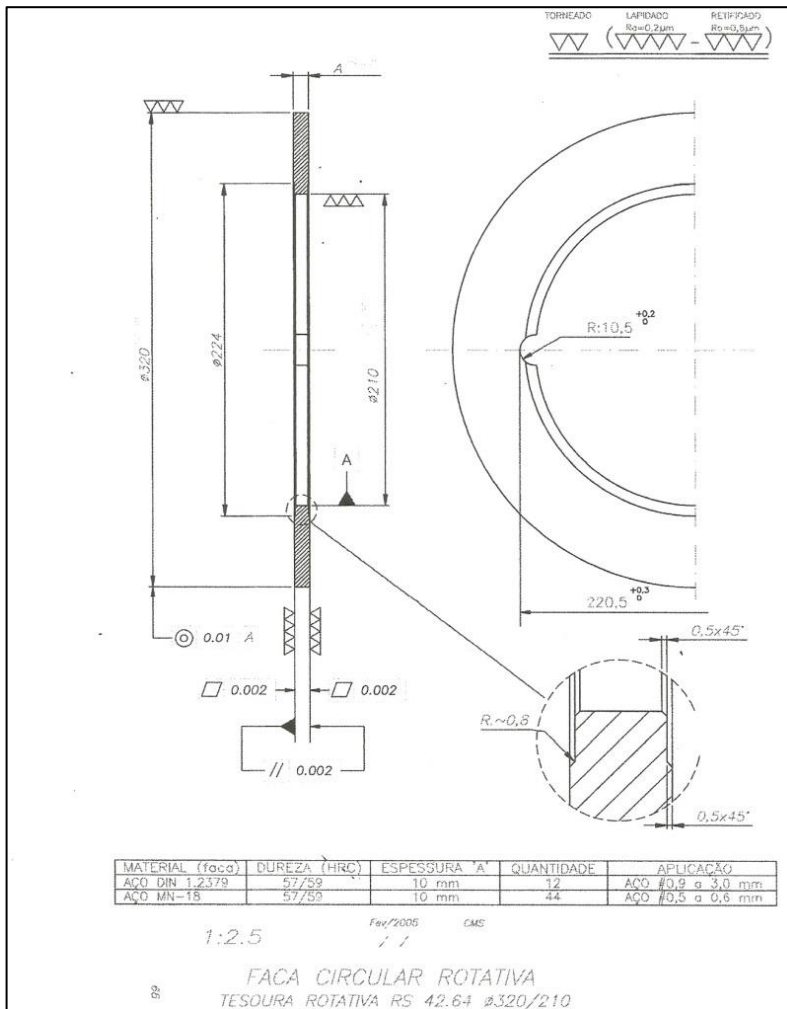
Desenho de Faca de Corte Utilizada para Processamento de Bobinas
